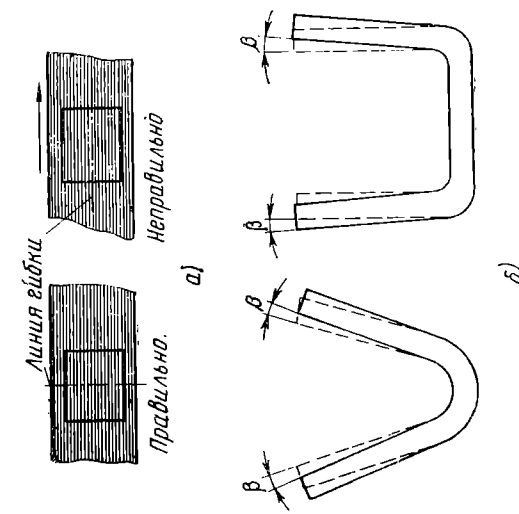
Расположение линий гибки (а) и направление волокон металла при гибке (б) (направление волокон металла указано стрелкой)
